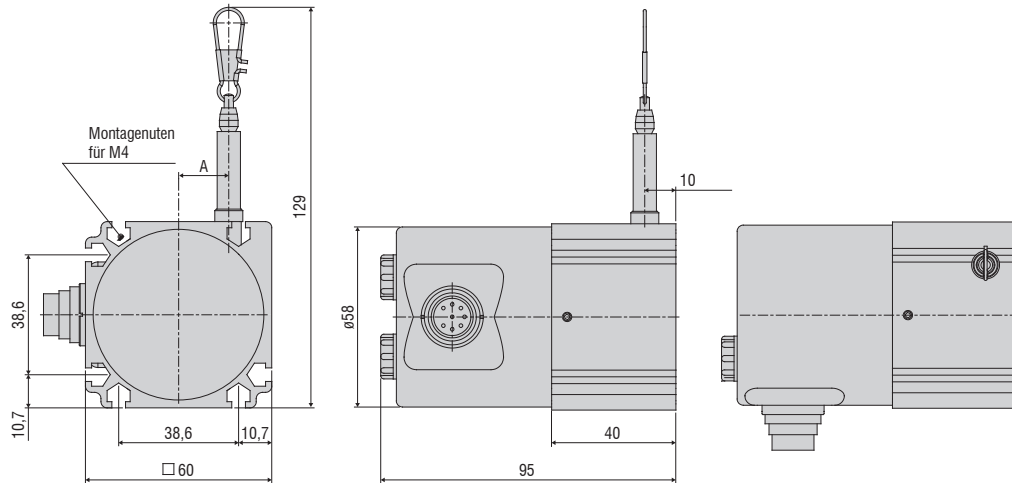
Maßzeichnung WDS- ... - P60 - SR - U/I, Abmessungen in mm
